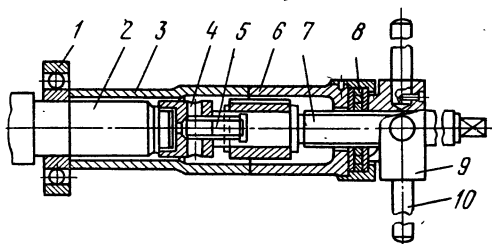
Винтовое приспособление для напрессовки подшипников:
